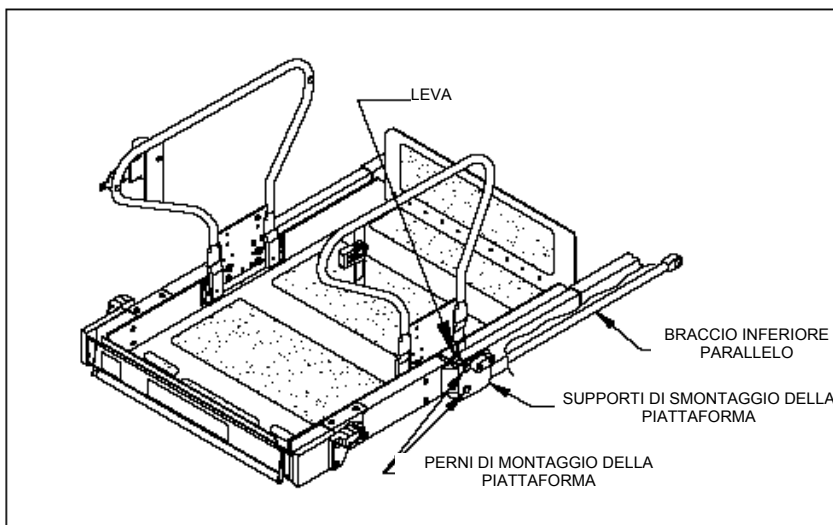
SEPARAZIONE DEL TELAIO DI SOLLEVAMENTO DALLA PIATTAFORMA
